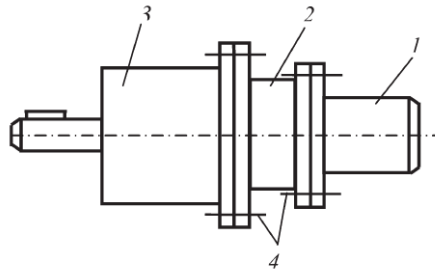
Компоновка мотор-вариатор-редуктора
